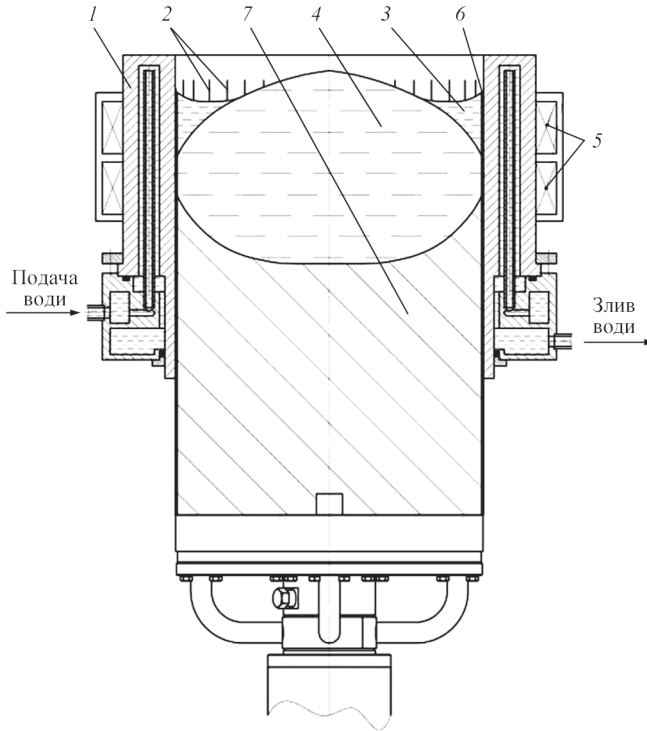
Схема секційного кристалізатора [56]: 1 — секція кристалізатора; 2 — зазор; 3 — шлакова ванна; 4 — рідкий метал; 5 — індуктор; 6 — твердий шлак; 7 — зливоч
